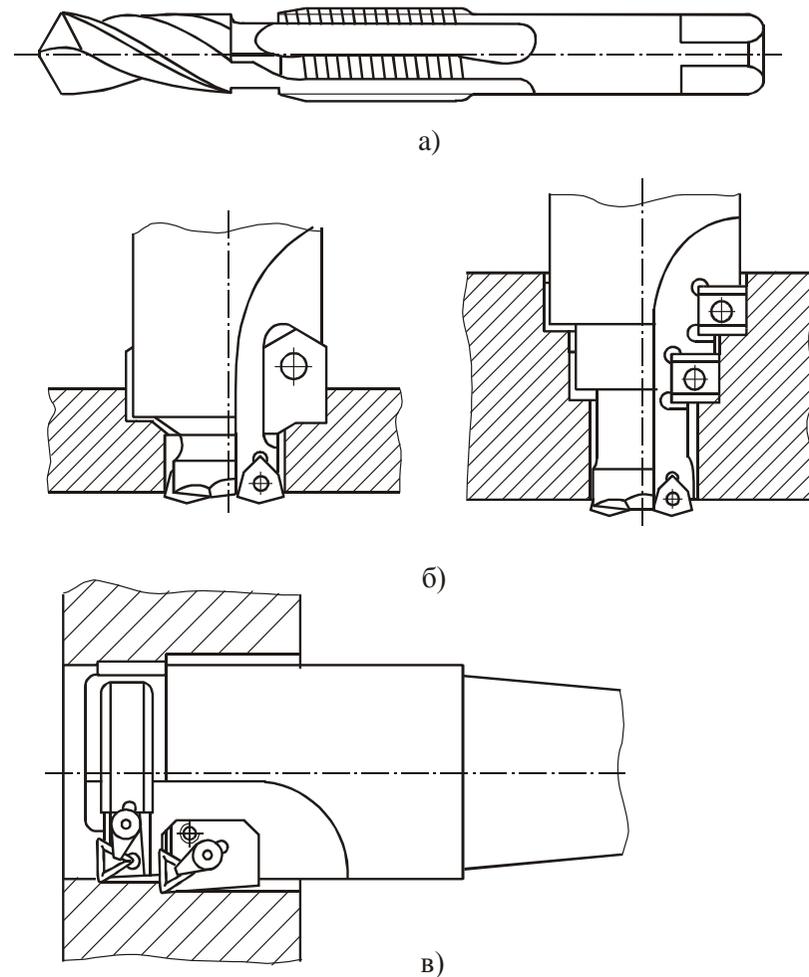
Комбинированные инструменты: *а* – сверло-метчик; *б* – сверло-зенкер; *в* – расточная оправка, оснащенная твердосплавными СМП
